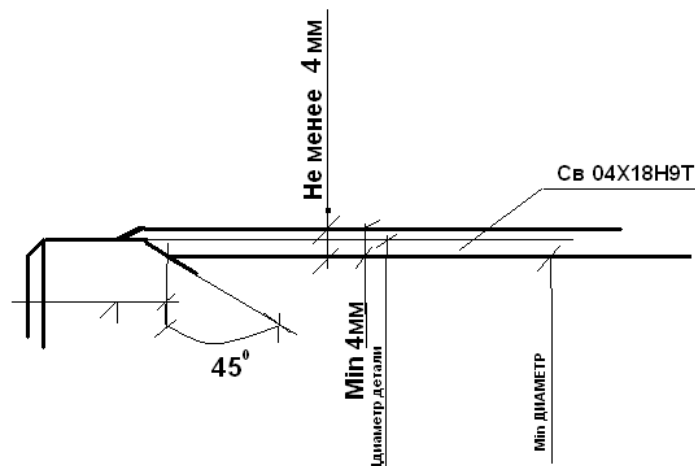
Способ автоматической наплавки проволокой марки Св-04X18Н9Т диаметром 2-3мм под слоем флюса марки АН-26 на наружные цилиндрические поверхности детали из материала чугуна.
